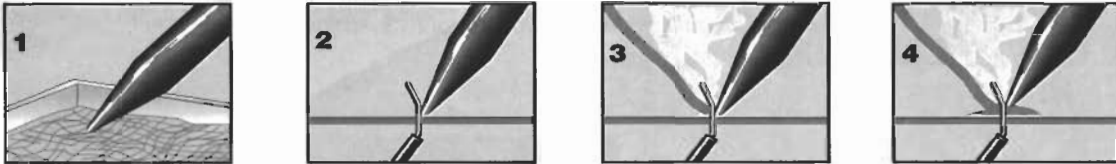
Como soldar sobre tarjetas de circuito impreso. Nuevamente, caliente la punta del cautín, límpiela con una esponja húmeda (1) y estáñela. Para soldar, caliente con la punta del cautín el terminal del componente y la pista del circuito impreso (2), aplique la soldadura (3) y permita que fluya uniformemente sobre la unión (4). Retire la soldadura y el cautín.
